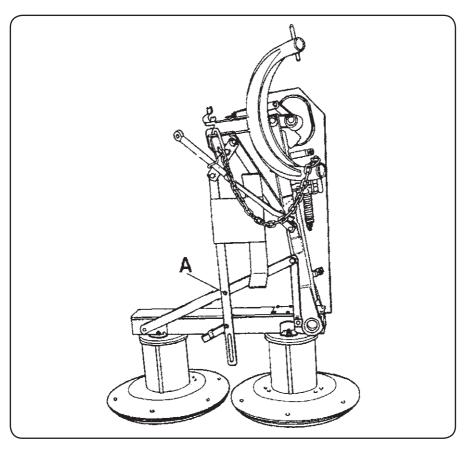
Установка косилки Z-178 для траспортировки в вертикальном положении.
